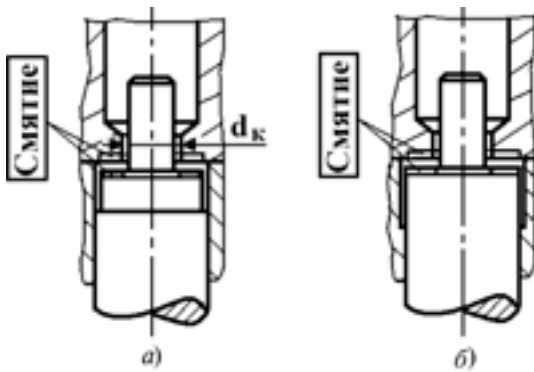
Схемы деформации (смятия) торцевых поверхностей иглы и корпуса форсунки при уменьшении диаметра иглы (а) и расточке поверхности корпуса распылителя (б)
